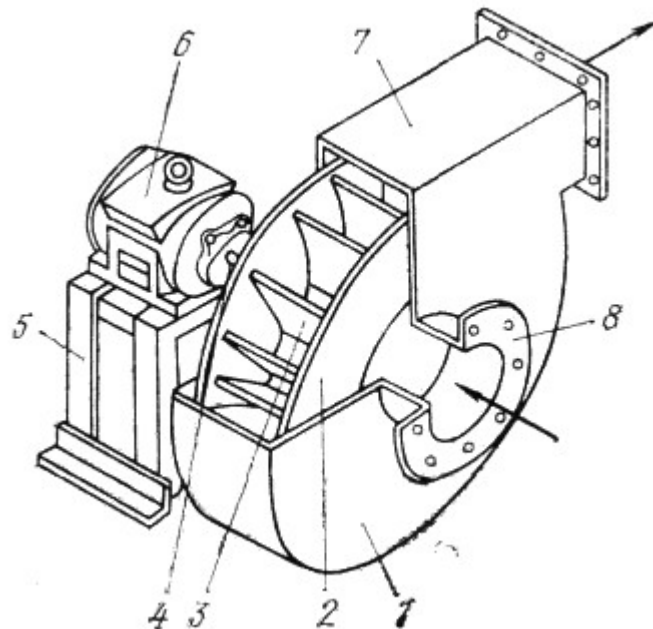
Конструкція радіального вентилятора: 1 – корпус; 2 – робоче колесо; 3 – лопаті роботоного колеса; 4 – ось вентилятора; 5 – станина; 6 – двигун; 7 – вихлопний патрубок; 8 – фланець всмоктуючого патрубка.
